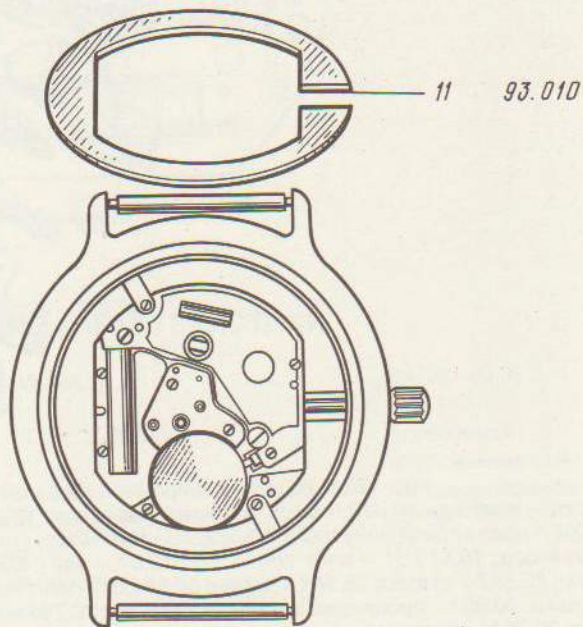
4 – винт скобы крепления; 5 – скоба крепления; 11 – кольцо крепления механизма
